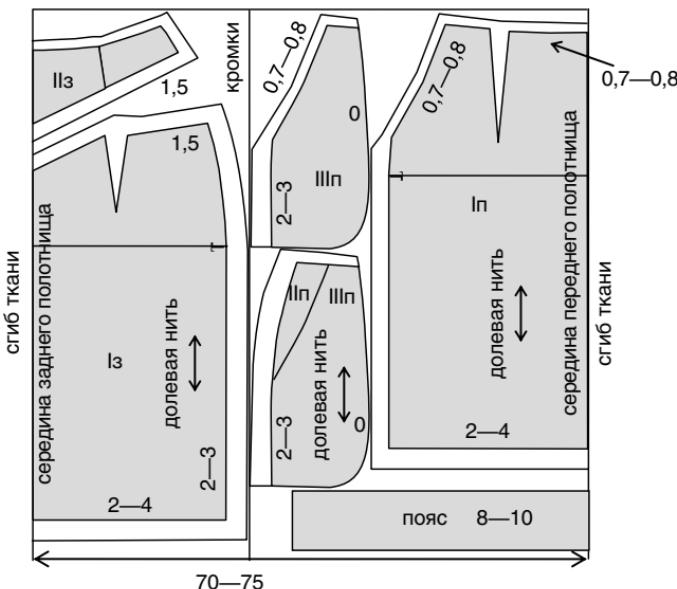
Раскладка на ткани выкроек юбки с подрезными карманами и кокеткой углом на заднем полотнище
